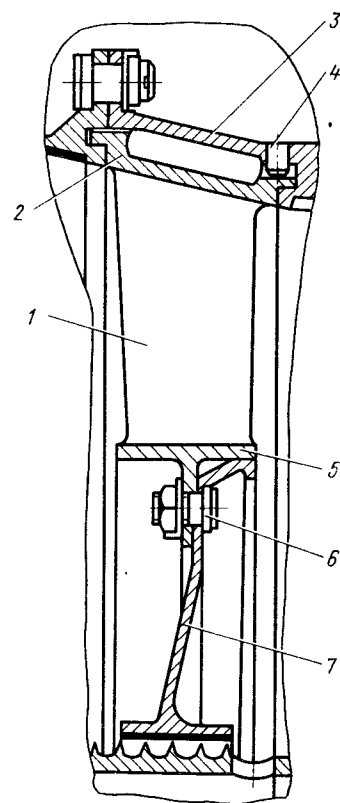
Разборный направляющий аппарат с жестким креплением к нижнему кольцу
